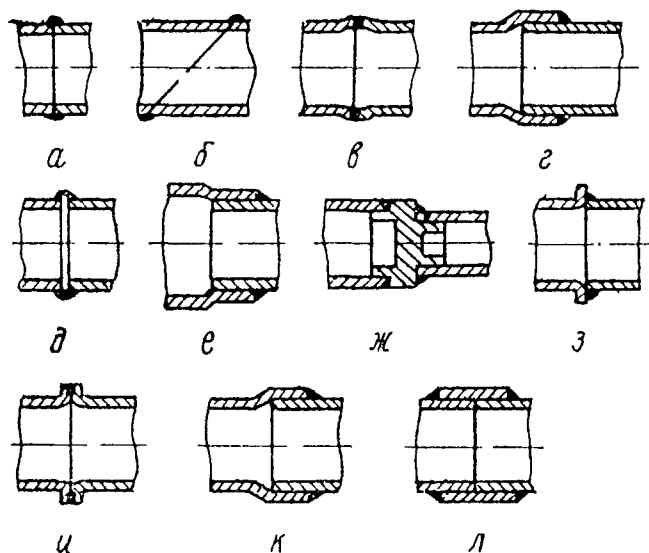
Способы сварки труб и трубопроводов
